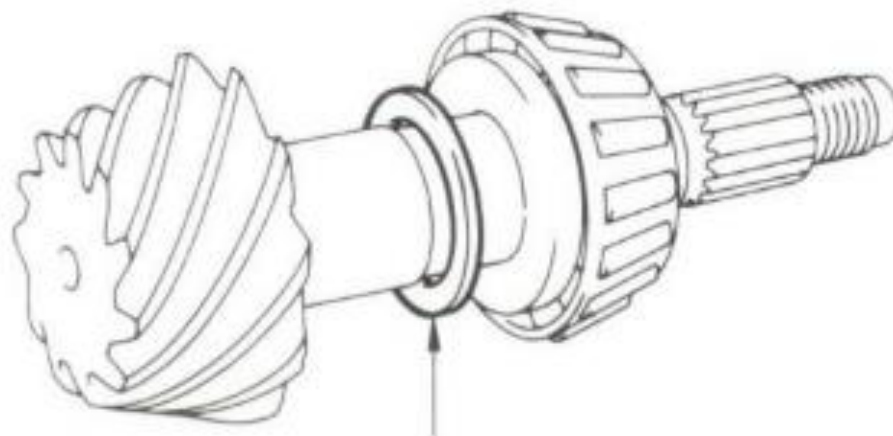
Регулювальна прокладка шестерні для встановлення правильного зачеплення коліс шестерні з головним редуктором.
